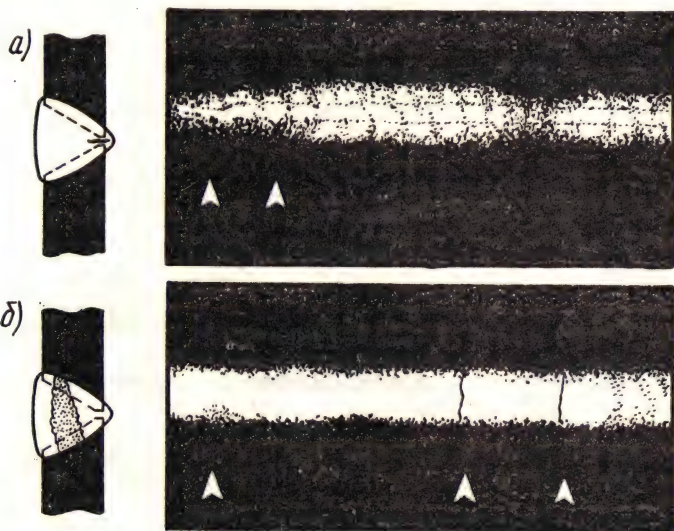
Схема и рентгеновский снимок сварного шва с продольной (*а*) и поперечной (*б*) трещинами
